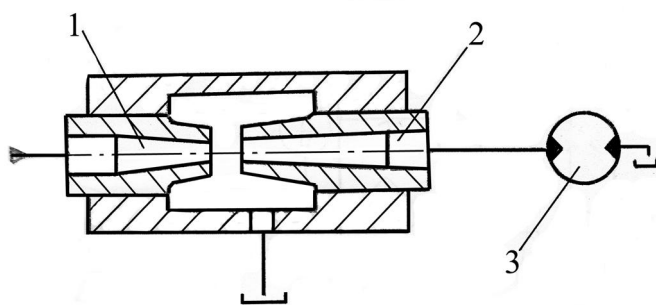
Схема струйного стабилизатора оборотов гидропривода: 1- питающее сопло; 2 – приемный канал; 3 – гидромотор
